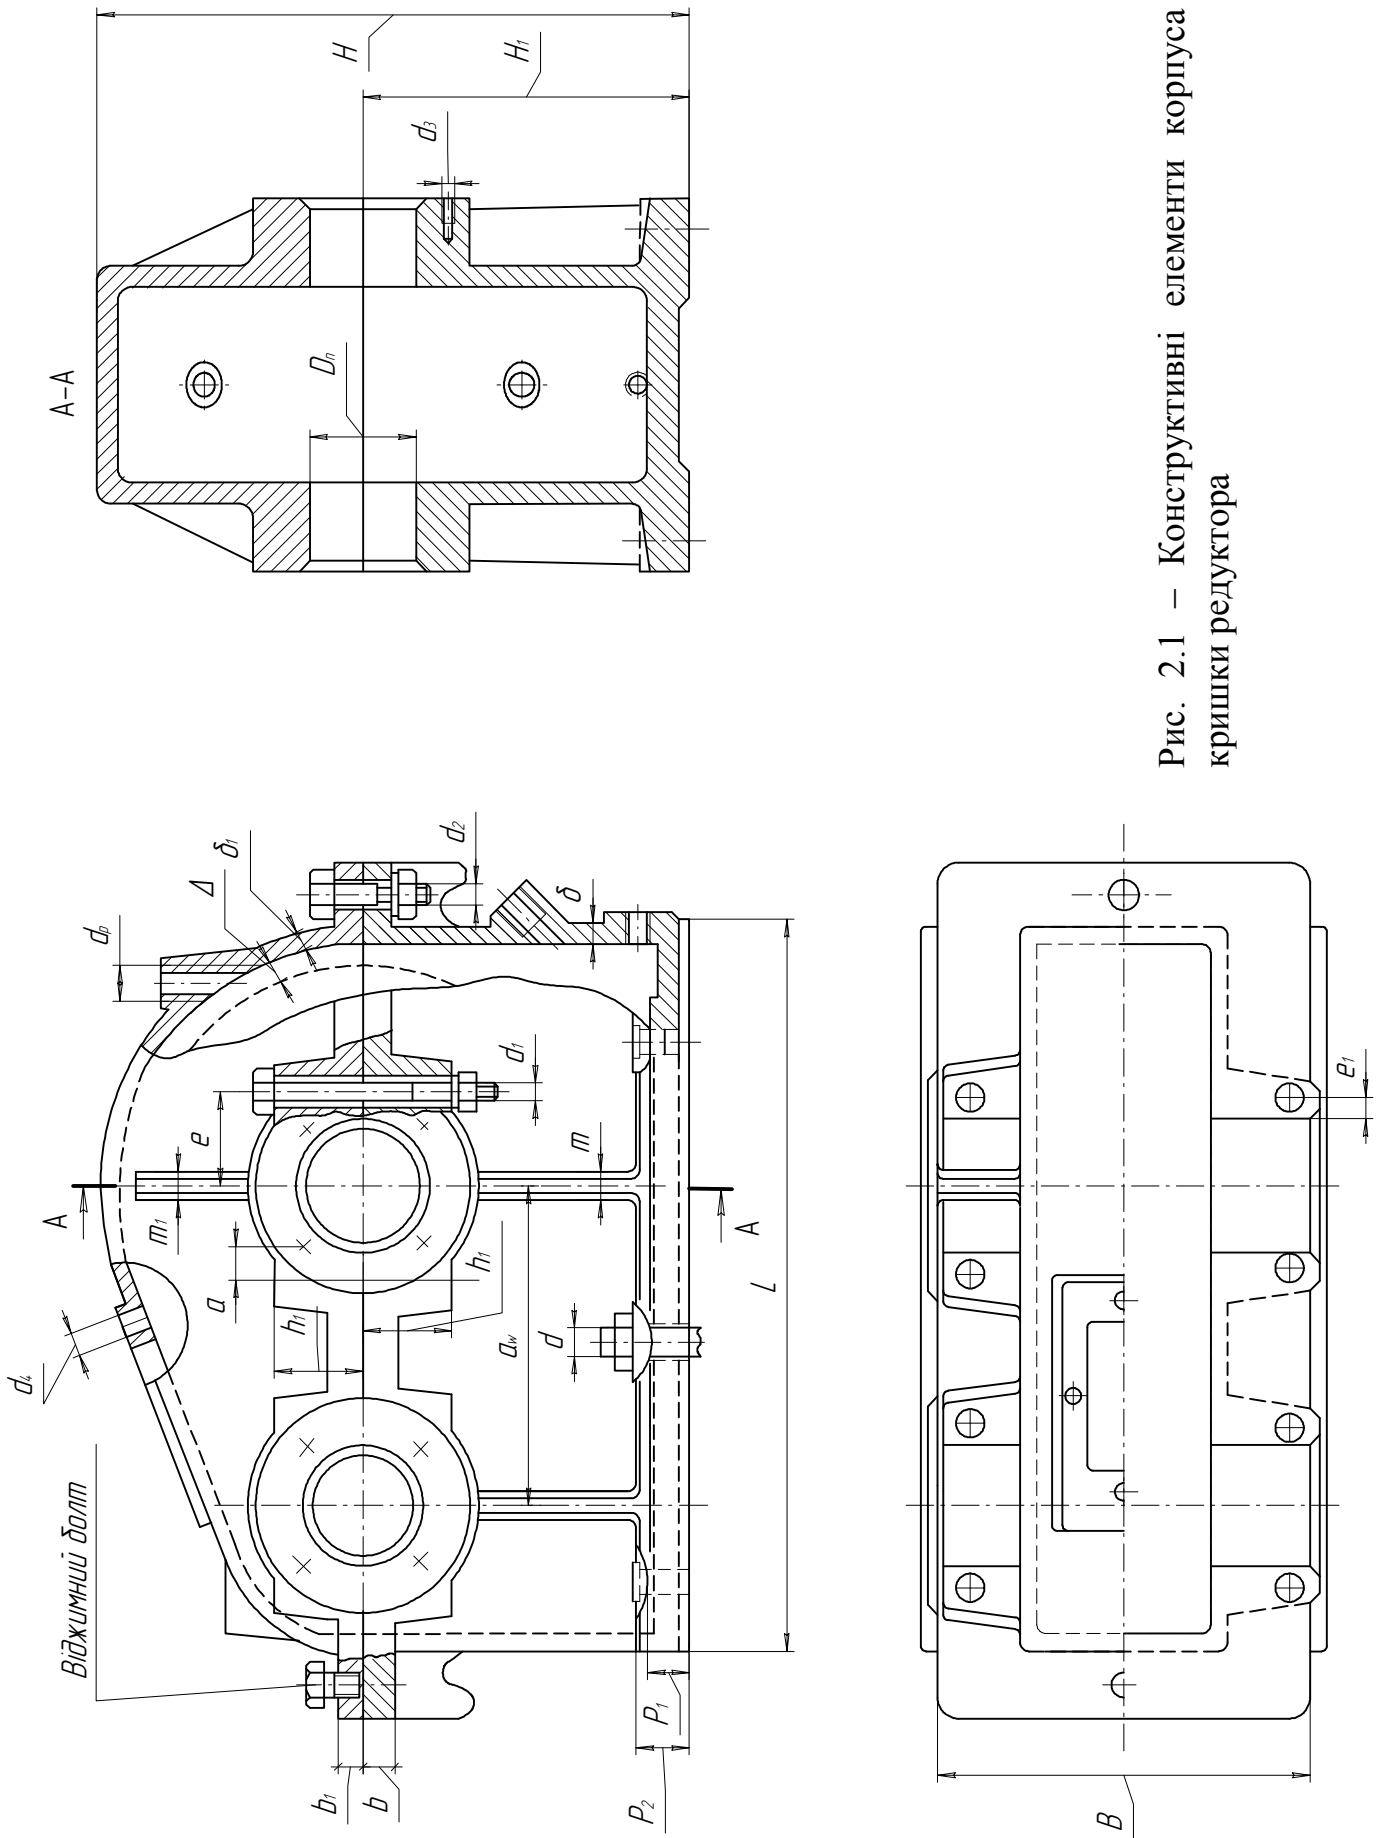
Конструктивні елементи корпусу і кришки редуктора
